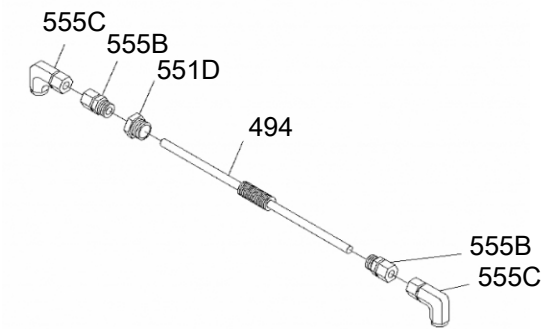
Lamellenrohrkühler Explosionszeichnung
